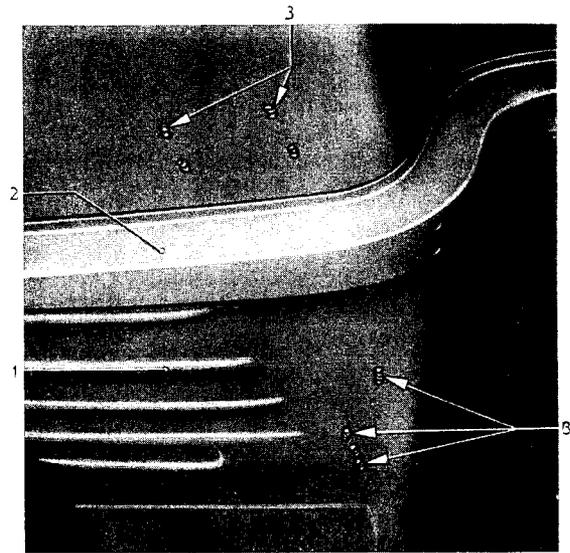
Löcher von ausgerissenen Schweißpunkten zugeschweißt, hier z. B. im Bodenblech
